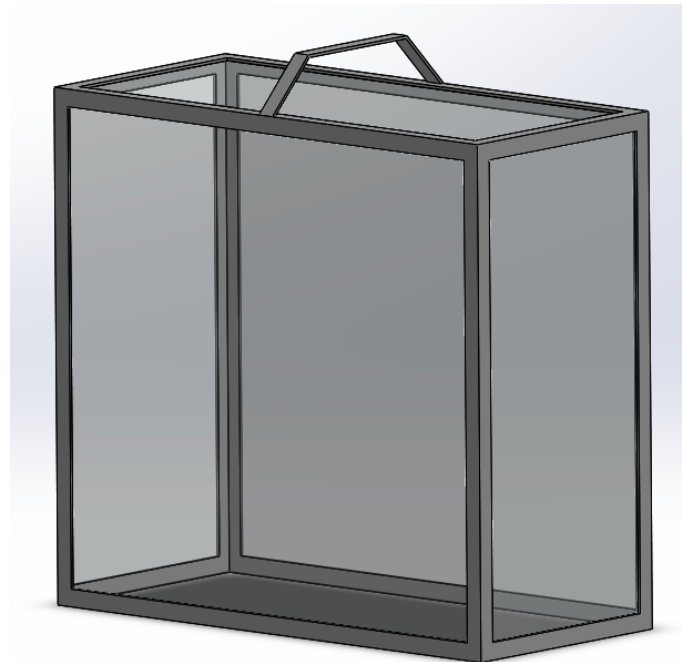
Propuesta de estructura de protección removible con malla metálica para cubrir zonas móviles.
